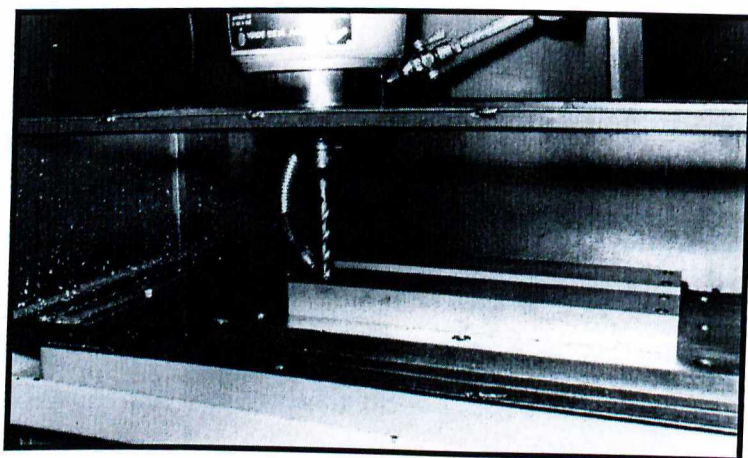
Montagem do sistema de fixação para realização dos testes.
